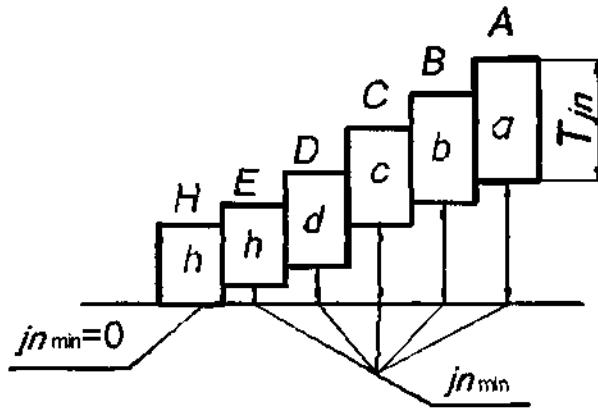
Схема расположения полей допусков на боковой зазор
